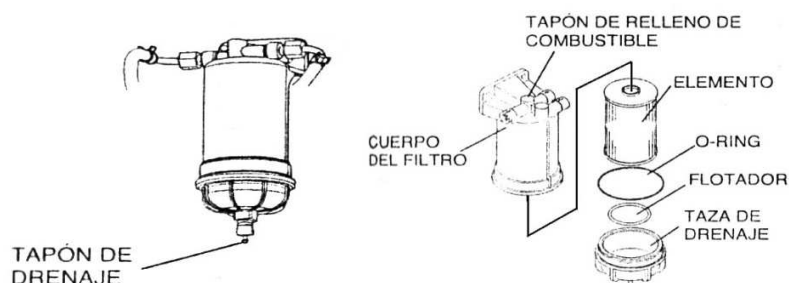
Despiece de las partes del filtro de combustible previo.
